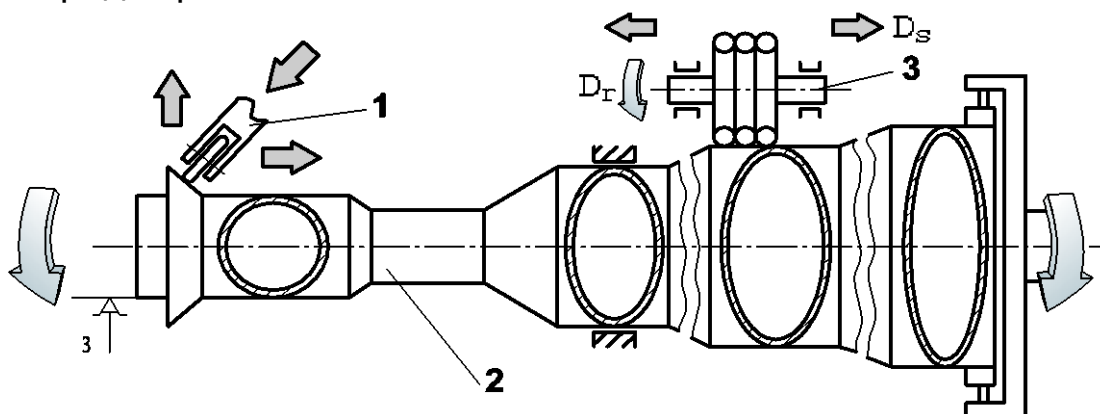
Схема обкатывания заготовки трубчатого лонжерона
